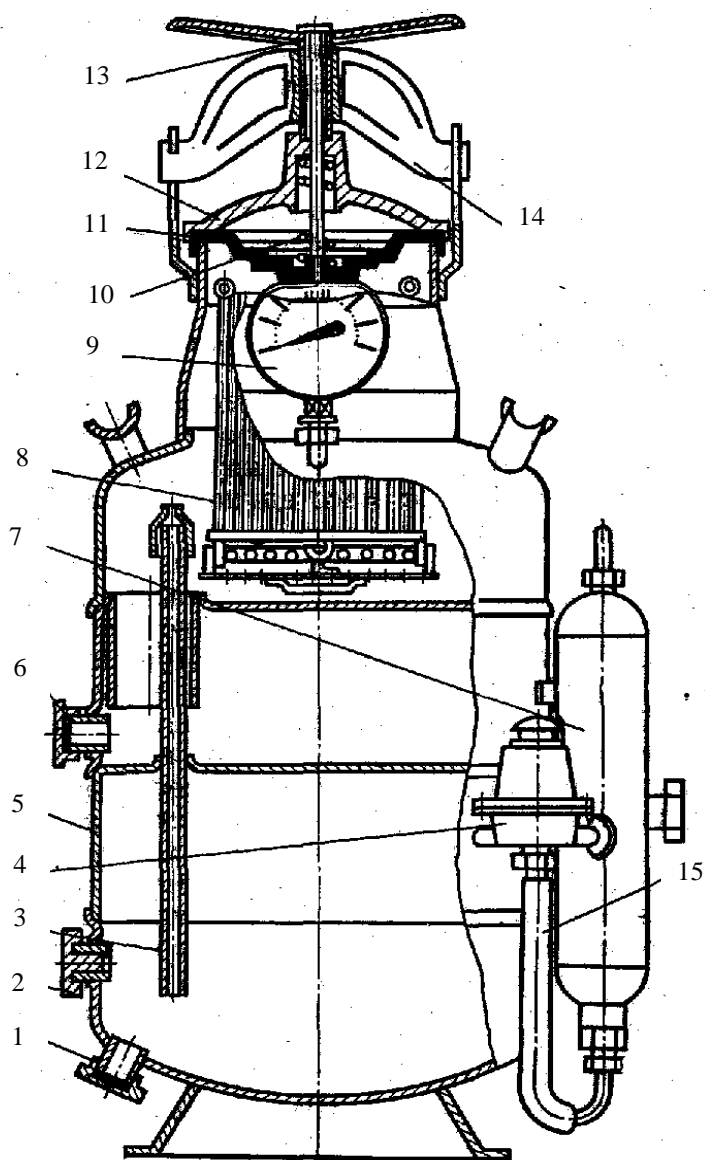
Ацетиленовый генератор АСП-1,25-6: 1, 6 – штуцеры; 2 – контрольная пробка; 3 – переливная трубка; 4 – предохранительный клапан; 5 – корпус генератора; 7 – предохранительный затвор; 8 – корзина; 9 – манометр; 10 – пружина; 11 – мембрана; 12 – крышка; 13 – винт; 14 – траверса; 15 – шланг
